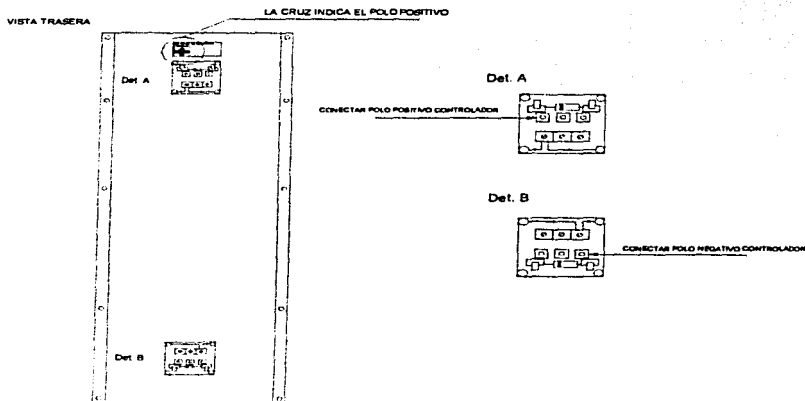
Se muestra la forma en que deben hacerse las conexiones de panel a controlador
